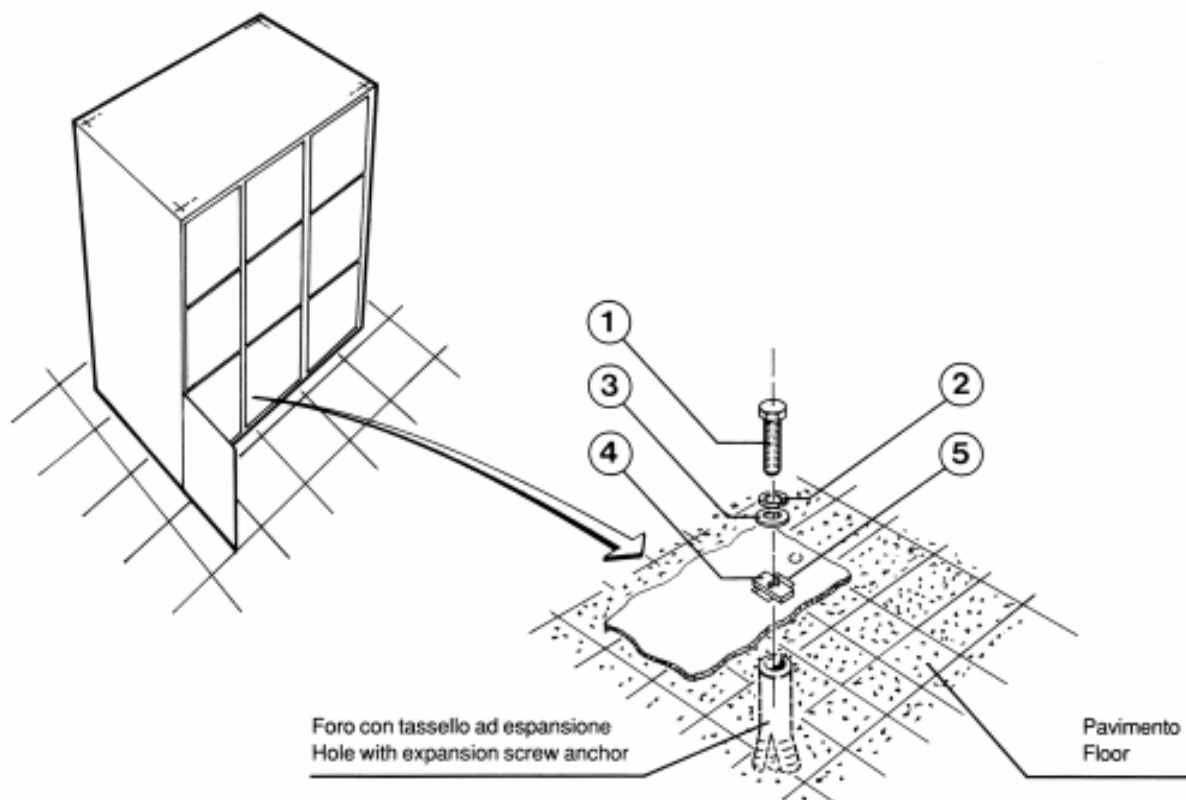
Fissaggio a pavimento con tasselli ad espansione
